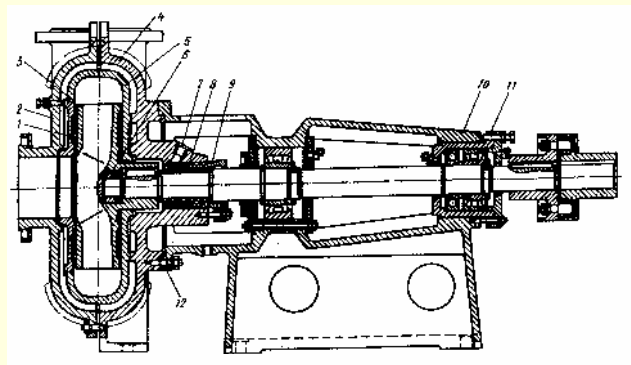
Грунтовый насос двухкорпусный типа ГрТ: 1 – защитный диск; 2, 4 – передняя и задняя половины корпуса; 3 – рабочее колесо; 5 – внутренний корпус; 6 – гайка; 7 – подвод промывной воды; 8 – сальниковое уплотнение; 9 – защитная втулка; 10 – кронштейн; 11 – стакан; 12 – фланец кронштейна
